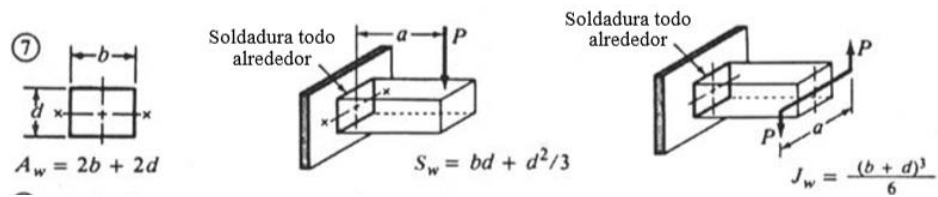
20. Factores geométricos para analizar la soldadura como una línea. Fuente: Norton,2012
